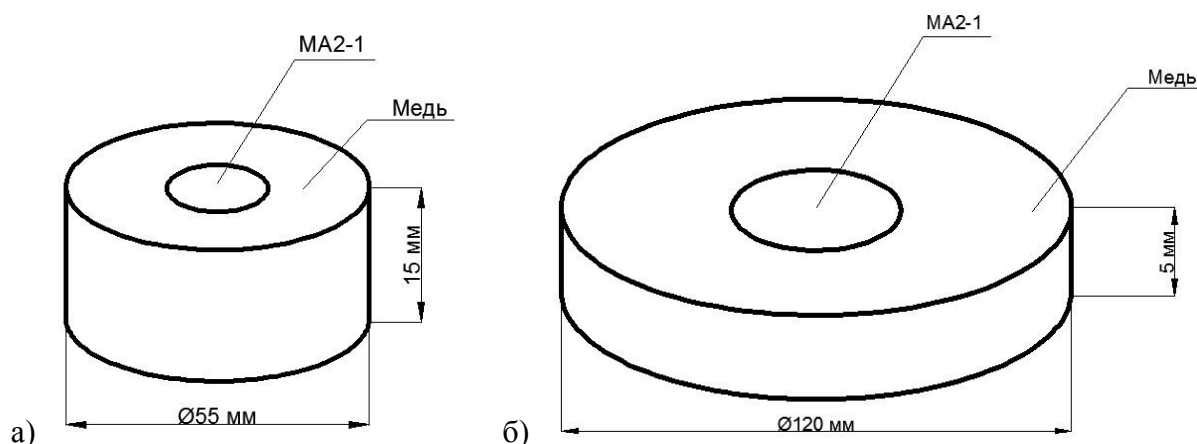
Схема заготовки: а) до штамповки; б) после штамповки.
